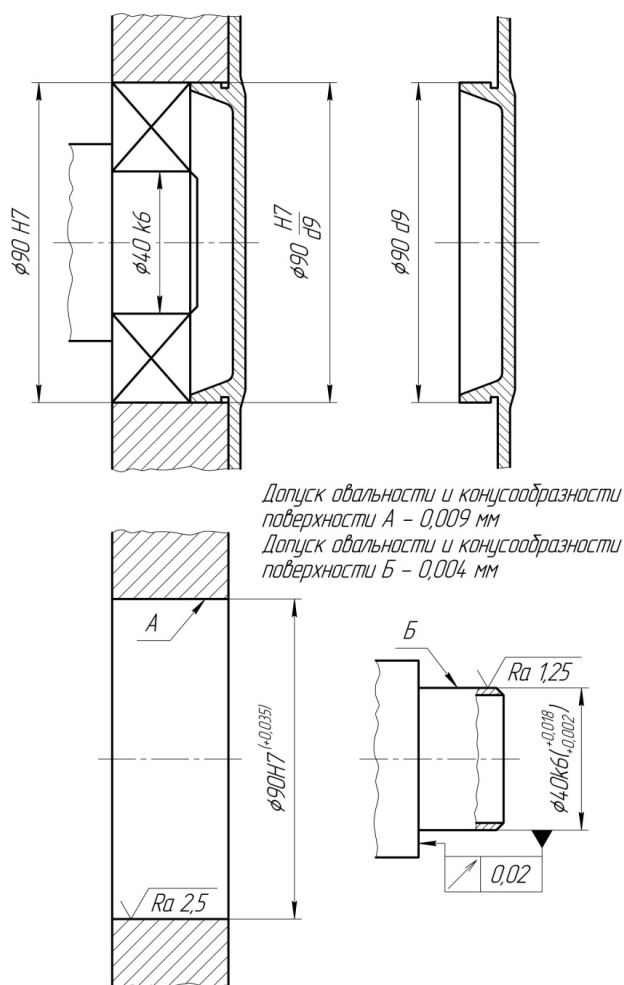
Обозначение посадок подшипников качения на сборочных чертежах, отклонений размеров и формы, расположения поверхностей на чертежах деталей
